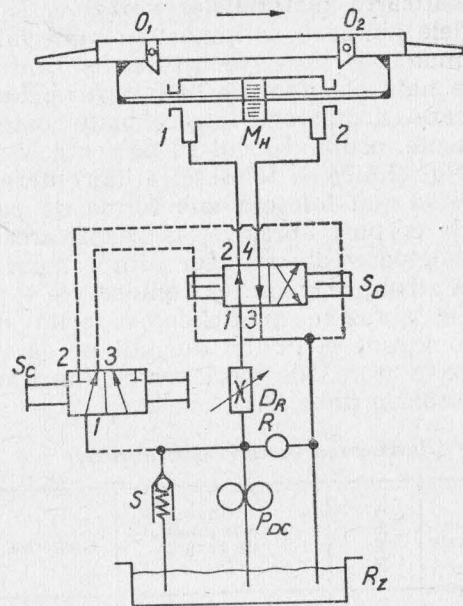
Schema hidraulică a unei mașini de rectificat plan.
